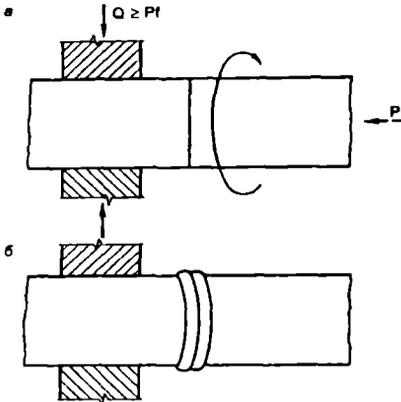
Принципиальная схема сварки трением:
